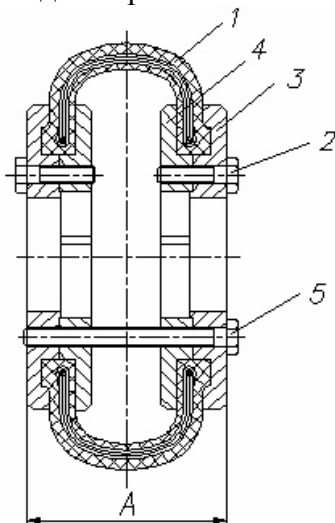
Резинокордная оболочка: 1 – многослойный упругий элемент; 2 – болты крепления фланцев; 3 – наружный фланец; 4 – внутренний фланец; 5 – технологические болты
